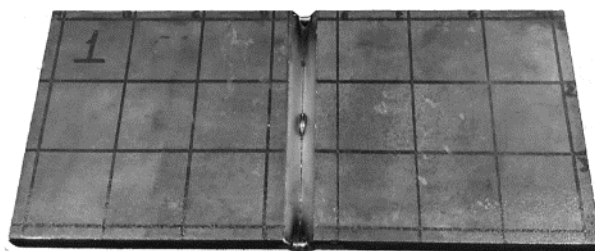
Preparação pré-soldadura dos corpos de prova para soldadura multipasses em juntas de topo
